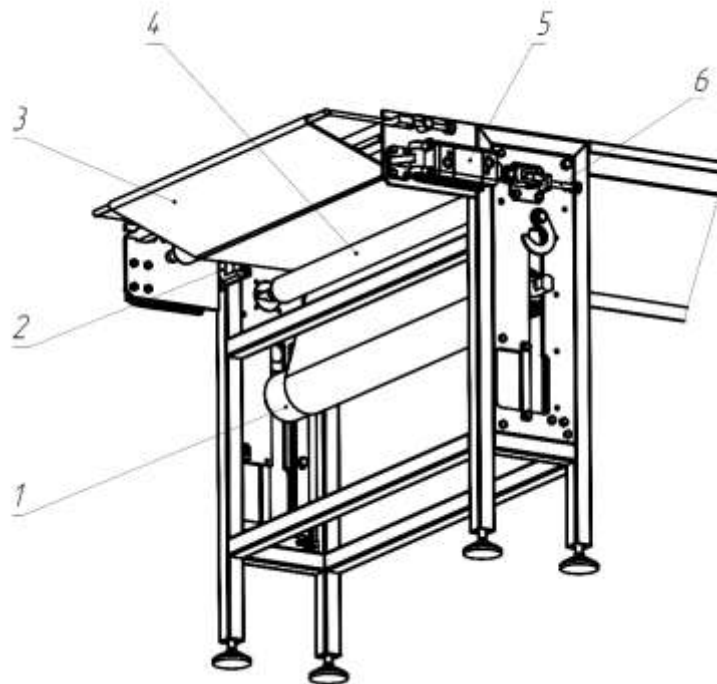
Вузол автоматичного вирівнювання положення стрічки з пневмоприводом: 1 – натяжний ролик, 2 – ролик вирівнювання положення стрічки, 3 – стрічка, 4 – давач, 5 – пневмоциліндр, 6 – гвинт регулювання ходу пневмоциліндра
